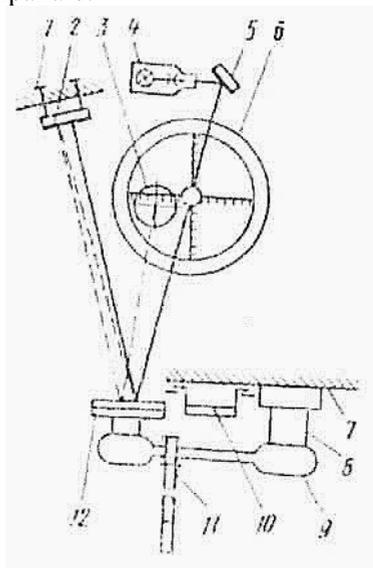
Принципиальная схема оптического прибора для проверки и правки шатунов
